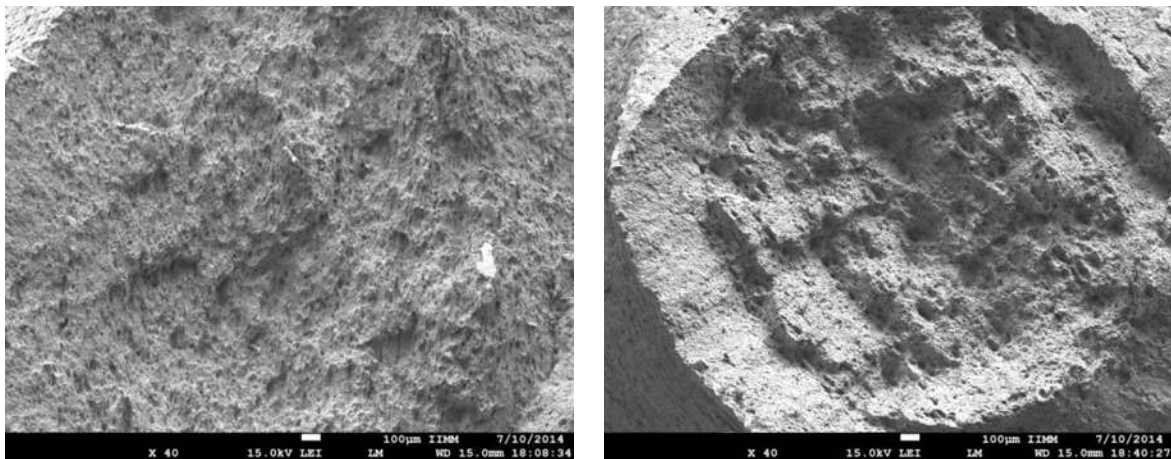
19.- Fractografía de la soldadura 1-1(unión simple, condición 1).
